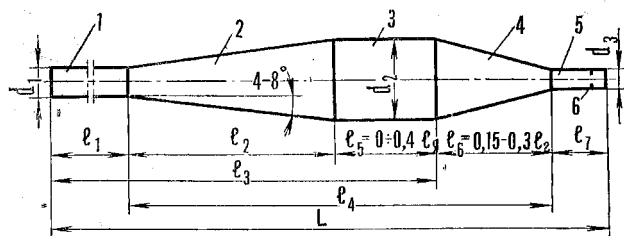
Система выпуска и исходные размеры ее элементов: 1 — выпускная труба; 2 — диффузор (конус расширения); 3 — цилиндрическая часть; 4 — конфузор (конус сжатия); 5 — выходная труба глушителя; 6 — шайба
